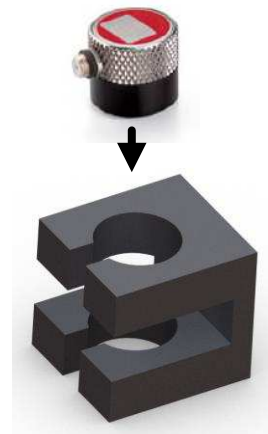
Vue en 3D de la pièce d'alignement usinée.
